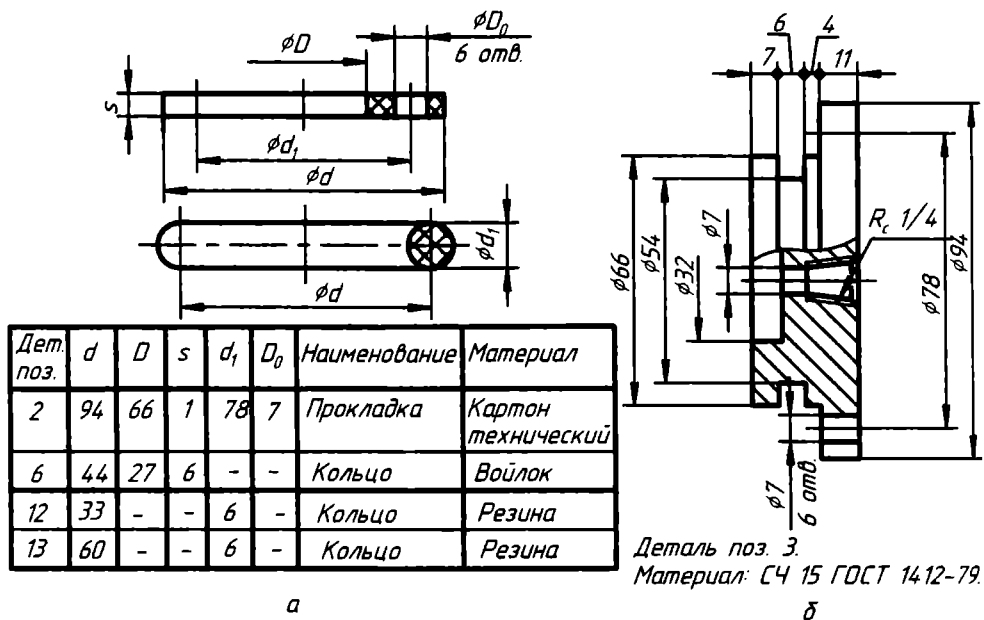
Чертежи: а — уплотнителей; б — крышки
